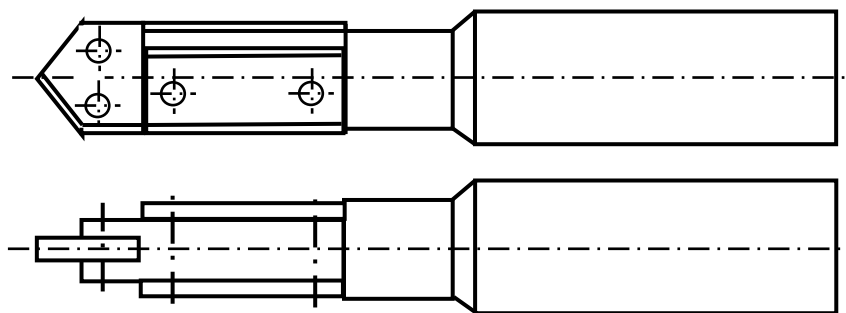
Фреза концевая со сменными твердосплавными ножами
